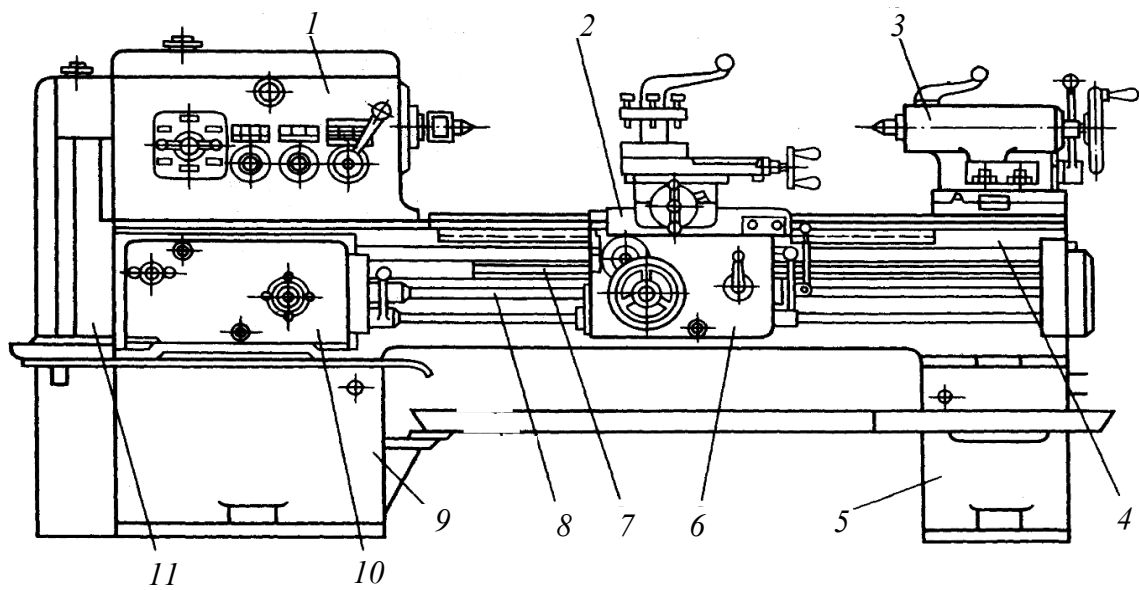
Токарно-гвинторізний верстат: 1 – передня бабка; 2 – поздовжній супорт; 3 – задня бабка; 4 – станина; 5 і 9 – тумби; 6 – фартух; 7 – ходовий гвинт; 8 – ходовий валик; 10 – коробка подач; 11 – гітари змінних шестерен
